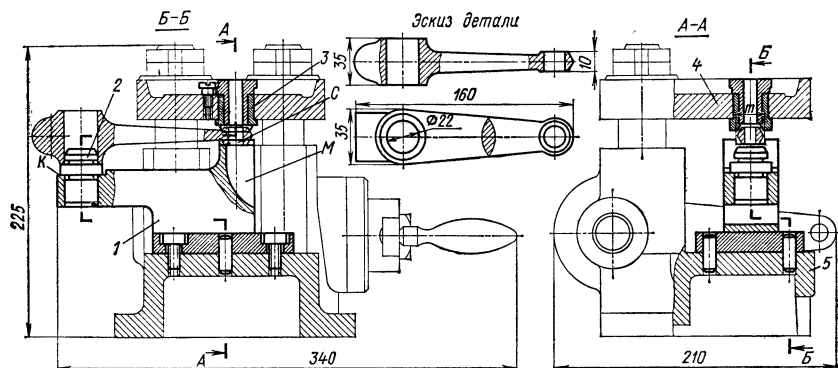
Наладка скальчатого кондуктора для обработки отверстия в малой головке шатуна
